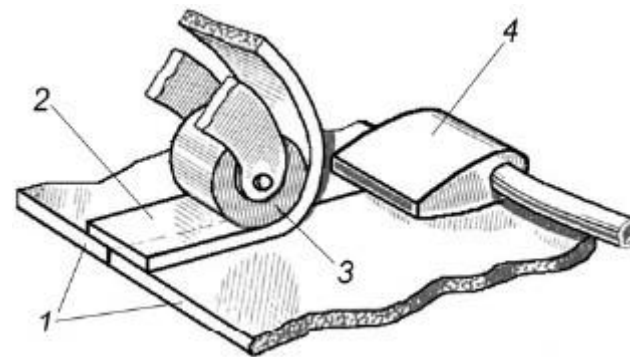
Стыковая сварка горелкой со щелевым соплом с применением присадки в виде ленты: 1 – основной материал; 2 – присадка в виде ленты; 3 – прижимной ролик; 4 – горелка со щелевым соплом
